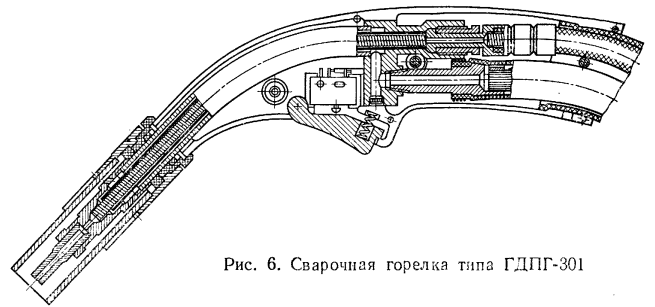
Сварочная горелка типа ГДПГ-301
